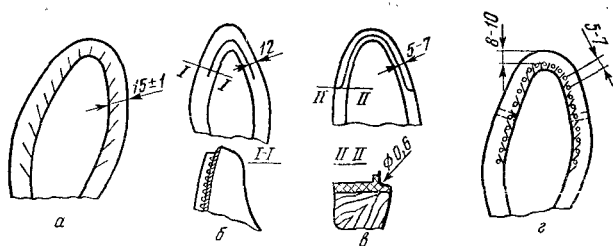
Схемы затяжки носочной или носочно-пучковой части заготовки верха обуви
